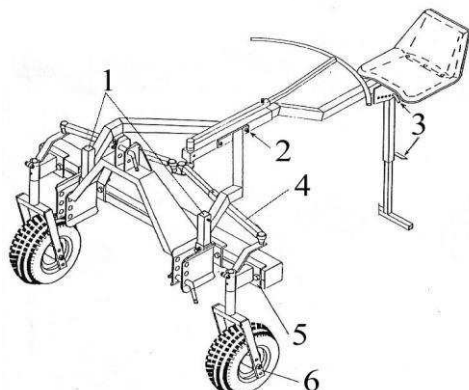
Рама культиватора ГС для монтажа опрыскивающего аппарата фирмы «Egedal»: 1 – место установки опрыскивающего аппарата; 2 – место крепления крана регулирования давления; 3 – сидение оператора с подножкой; 4 – поперечные тяги механизма руля; 5 – регулировка колеи; 6 – опорные управляемые колеса
